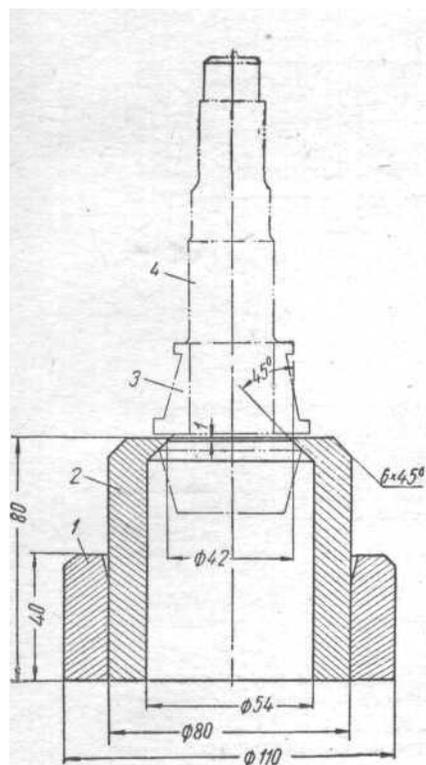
Приспособление для спрессовывания внутреннего кольца заднего подшипника вала ведущей шестерни:
